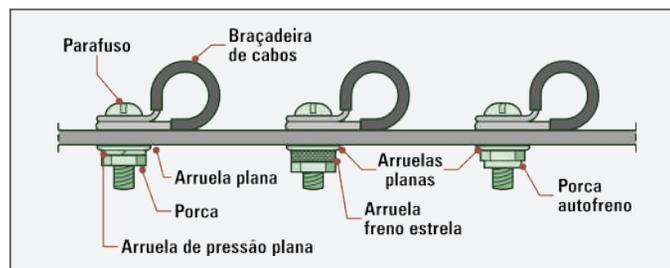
Ferragens típicas de montagem para braçadeiras de cabo
